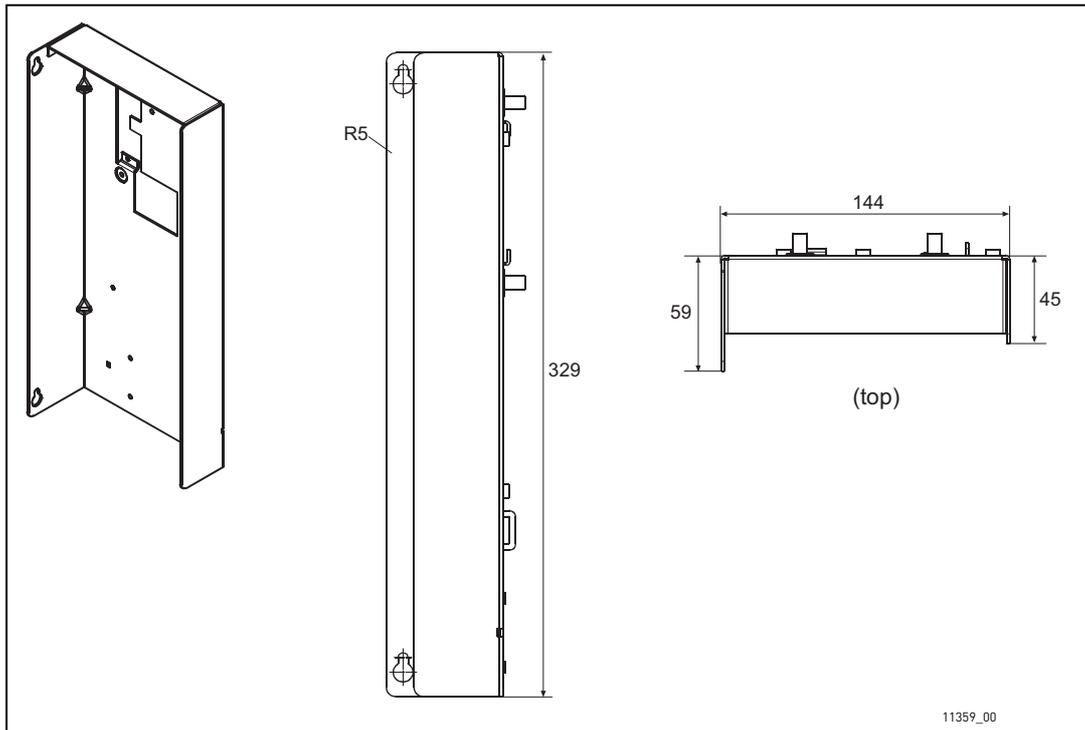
Dimensiones de la caja de montaje de la unidad de control
